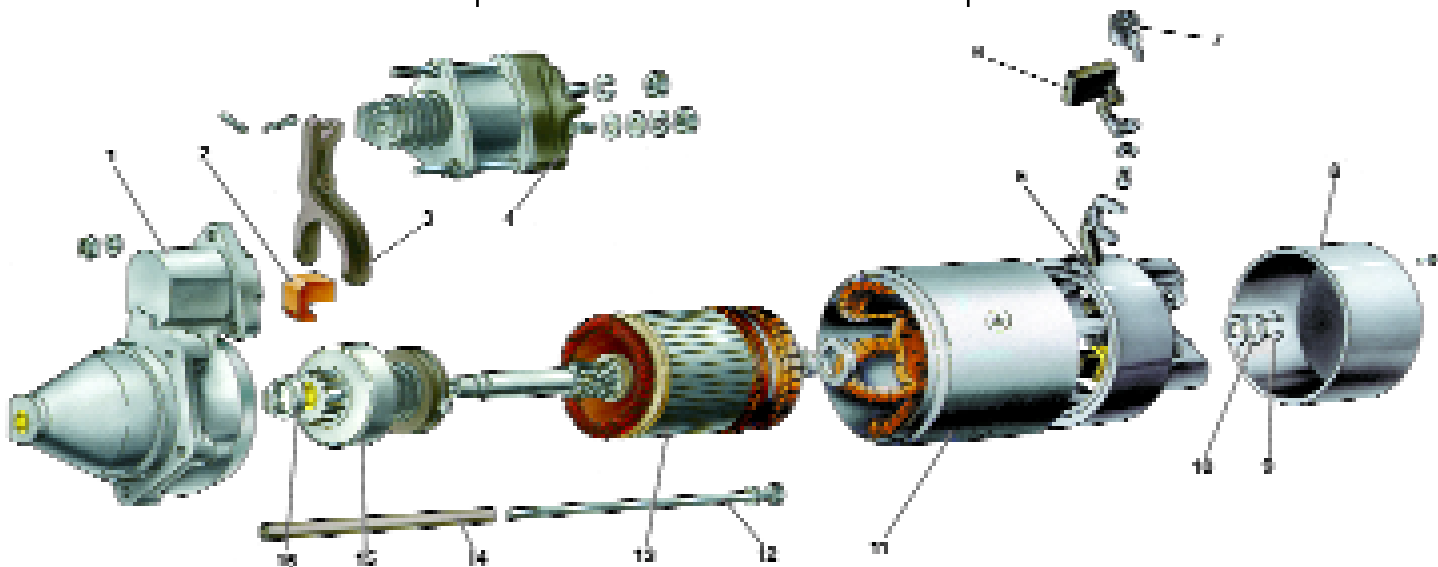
Детали стартера 35.3708: 1 – крышка со стороны привода с промежуточным кольцом; 2 – резиновая заглушка; 3 – рычаг привода; 4 – тяговое реле; 5 – крышка со стороны коллектора; 6 – щетка; 7 – пружина щетки; 8 – защитный кожух; 9 – стопорное кольцо; 10 – регулировочная шайба; 11 – корпус; 12 – стяжной болт; 13 – якорь; 14 – изолирующая трубка; 15 – обгонная муфта с шестерней привода; 16 – ограничительное кольцо
